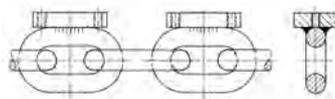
Einsatz mit angeschweißten Aufnahmen für austauschbare Mitnehmer, Verwendung z. B. in Schlachtbetrieben
